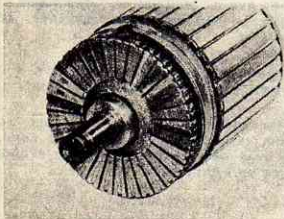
Якорь стартера 29.3708 с обгоревшими пластинами коллектора.
